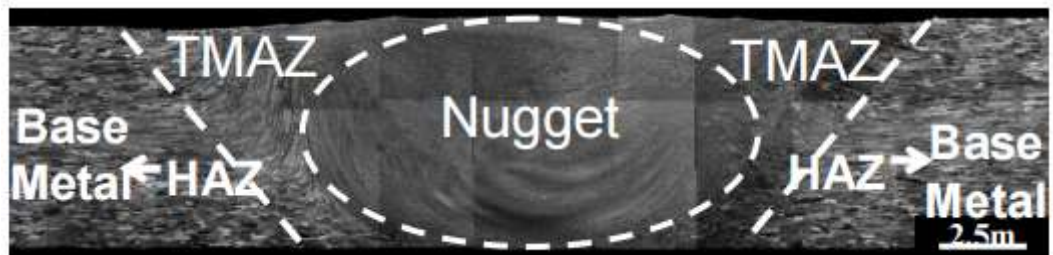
Zonas Metalúrgicas de una soldadura FSW (TMAZ Zona afectada termo-mecánicamente)
